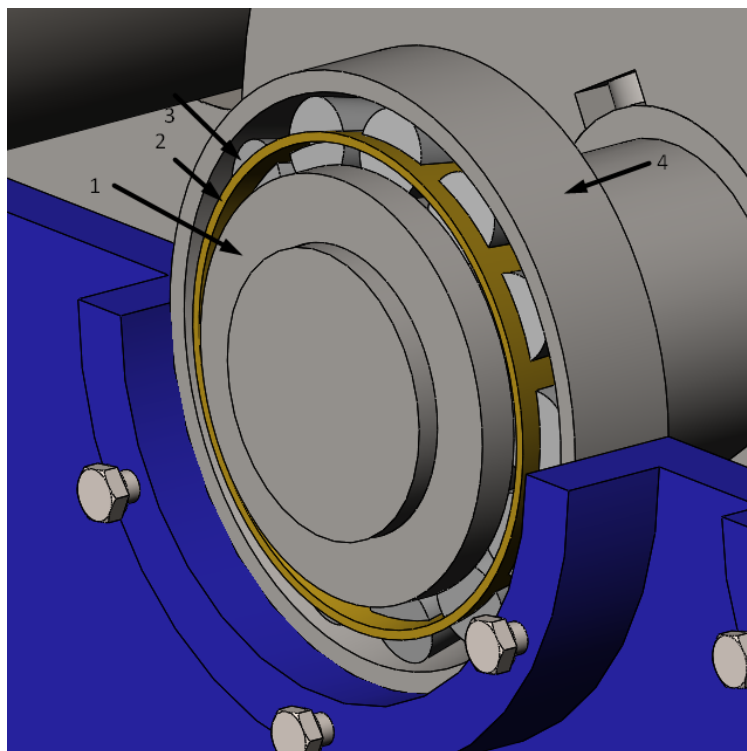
3D-модель роликового конічного підшипника проміжного валу редуктора
